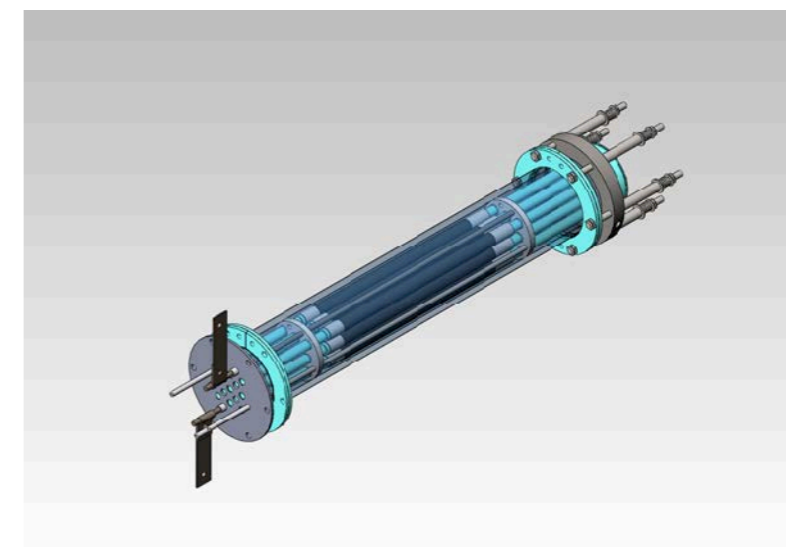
Внешний вид батареи ТОТЭ. Корпус батареи показан полупрозрачным.
